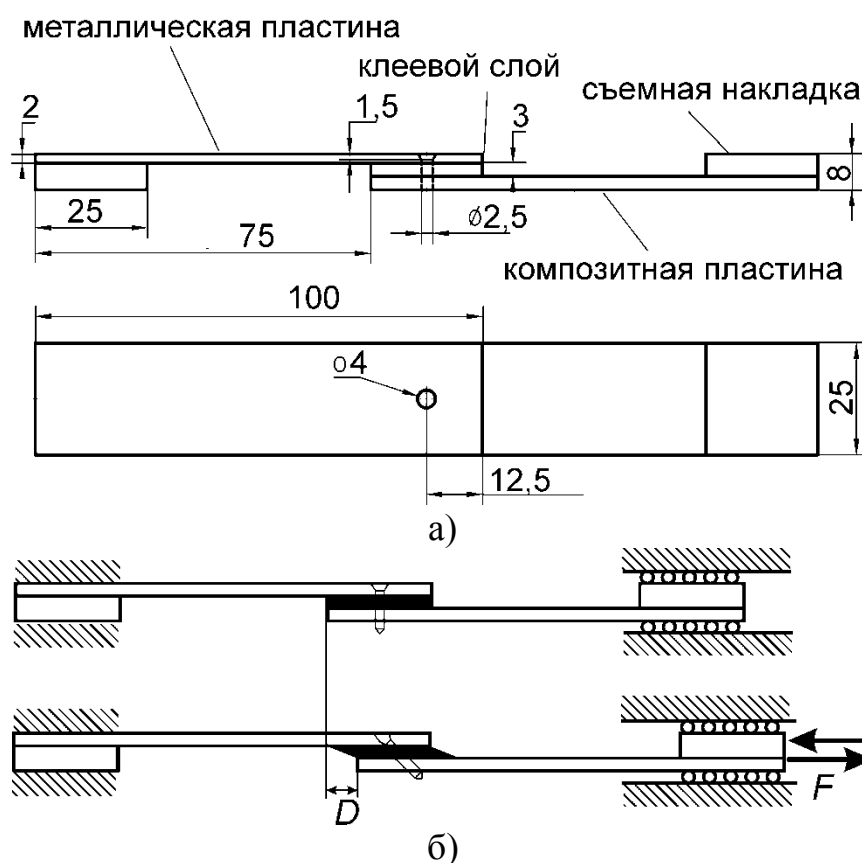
Образец нахлесточного соединения: а) эскиз; б) схема испытаний
